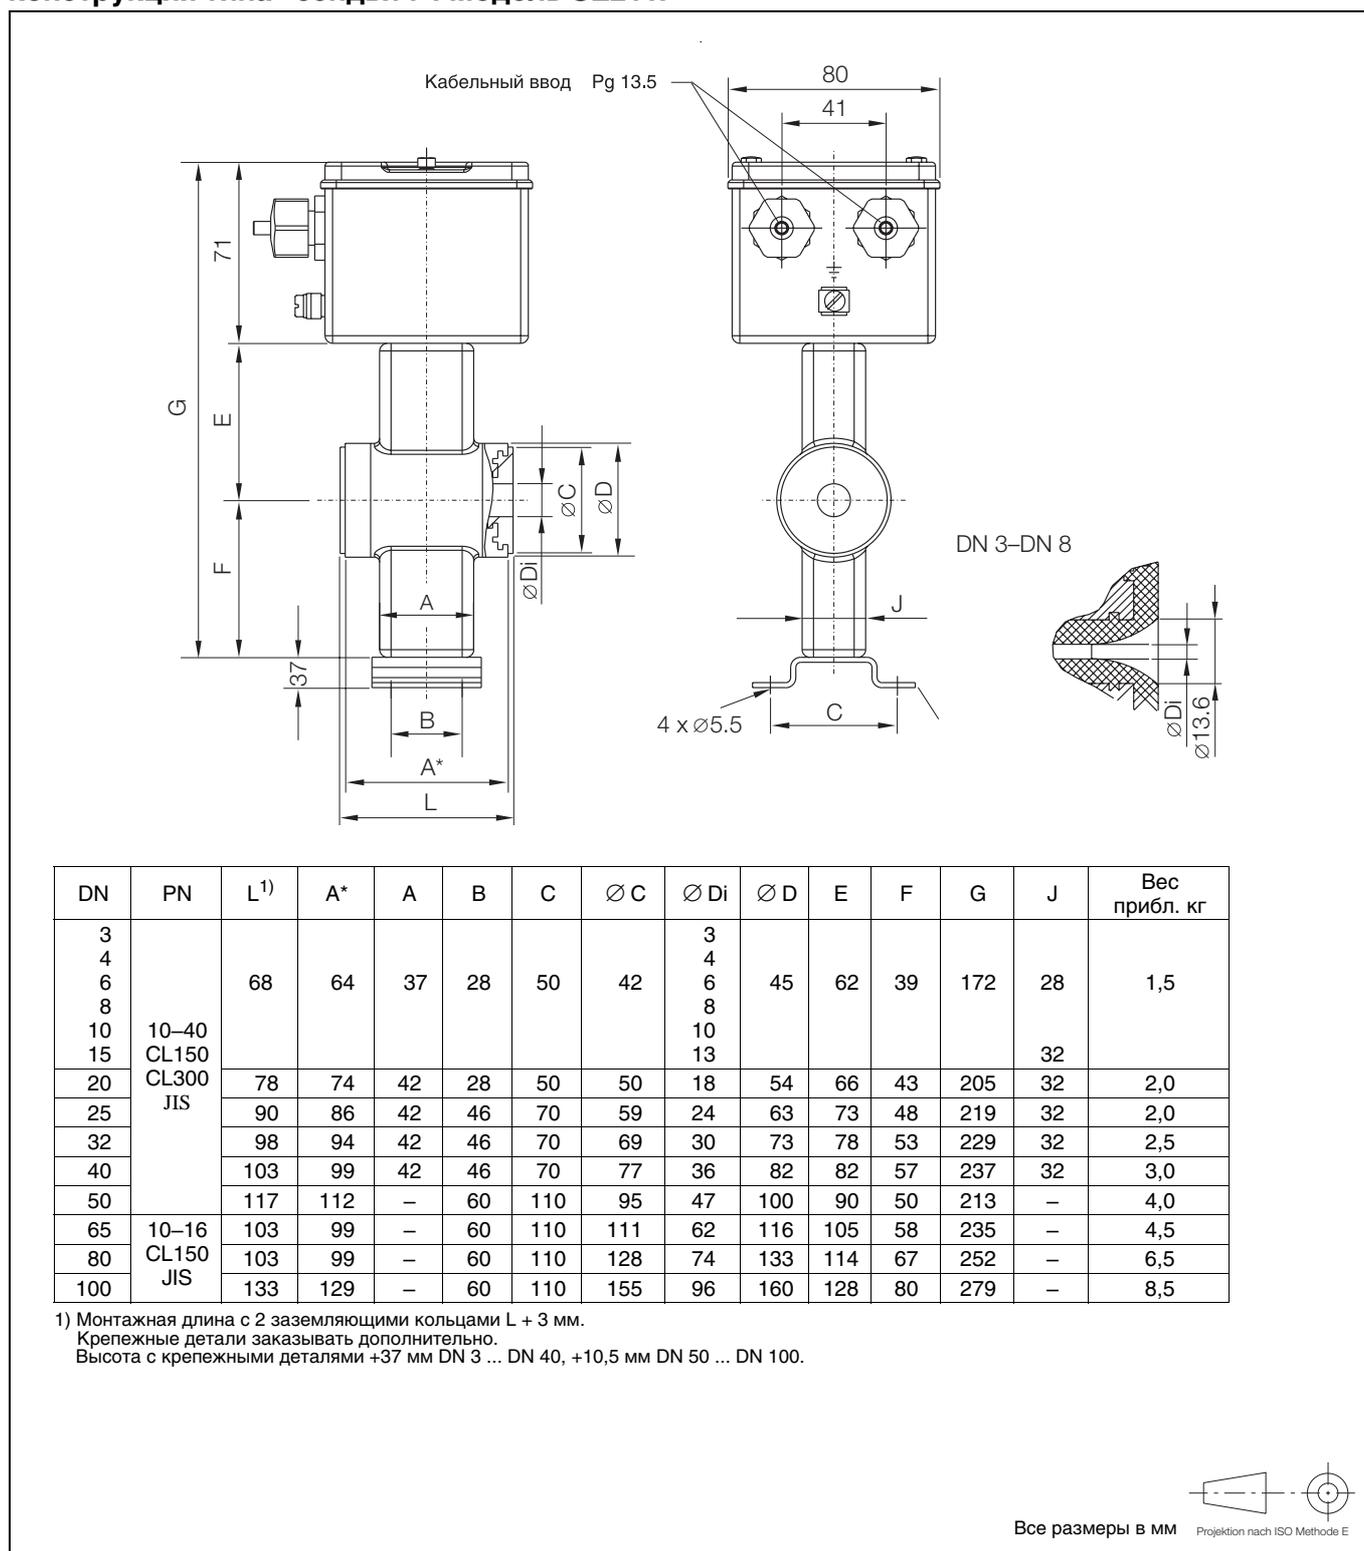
Первичный преобразователь DN 3 - DN 100, конструкция типа "сэндвич".
